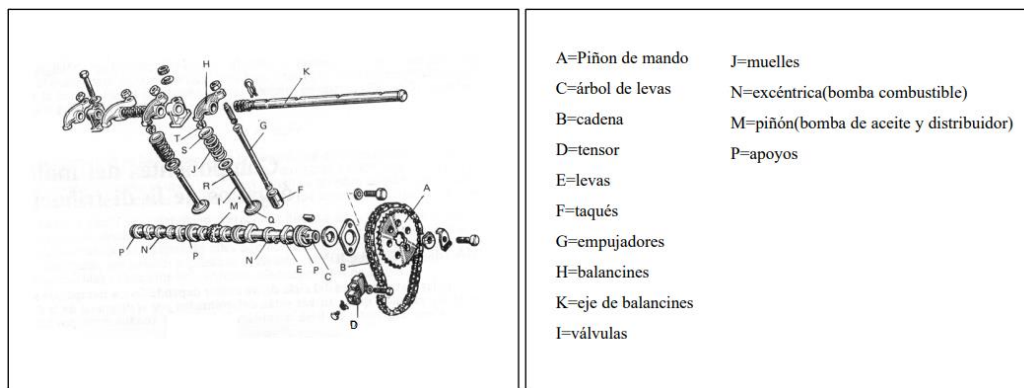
Explosionado y partes del Sistema de distribución (Más usado). Fuente: Ajuste de Motor [38]
